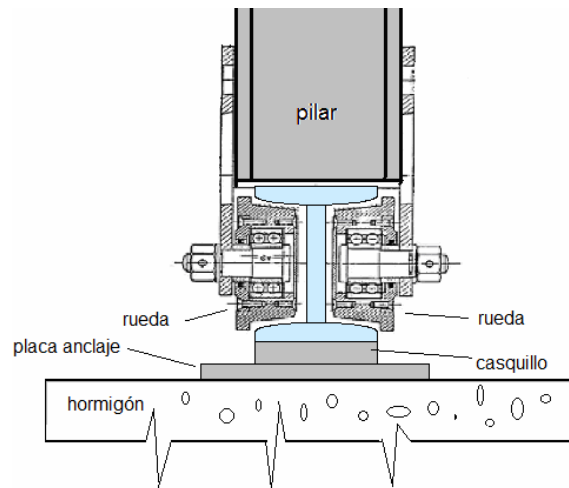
Dibujo explicativo del pilar, las ruedas y la viga carril
